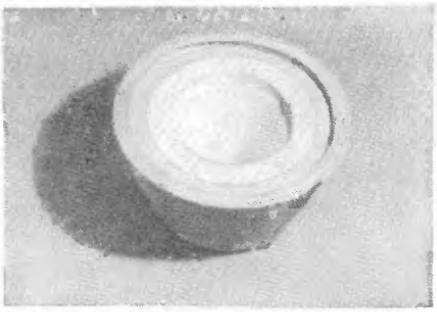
Обточенный кожух (с шарниром) и маточная форма
